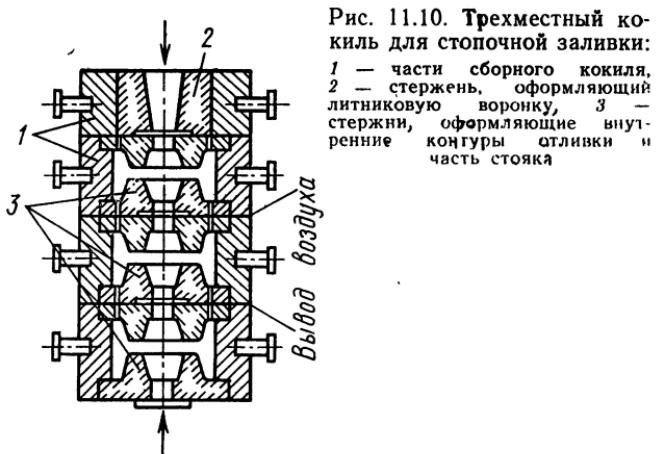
Трехместный кокиль для стопочной заливки:
